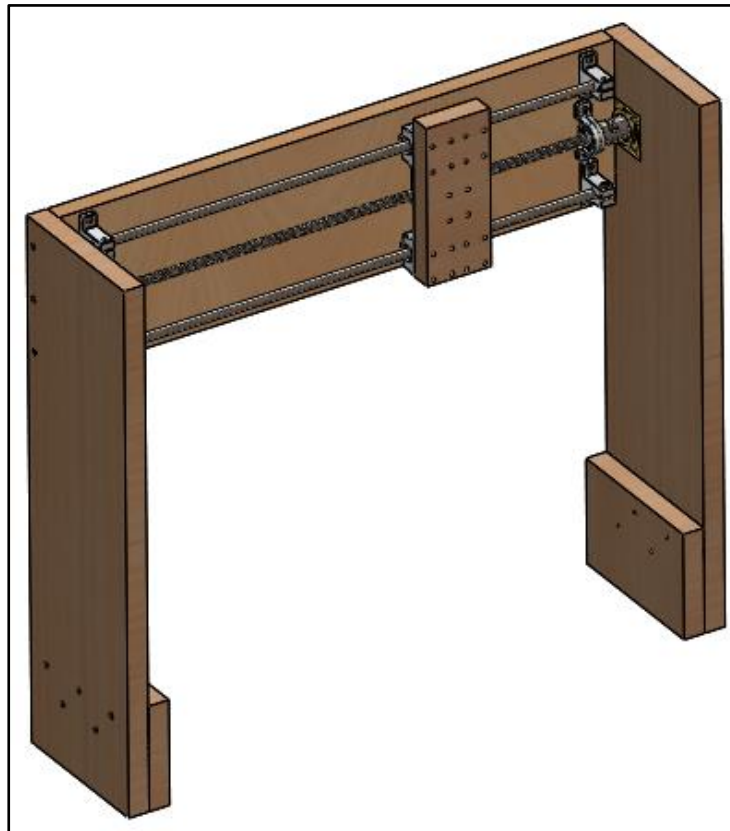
Vista isométrica del ensamblado completo de la estructura eje Y del módulo router CNC.
